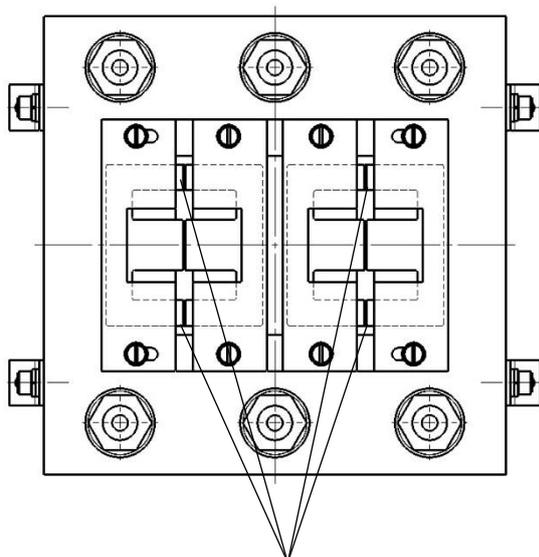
Draufsicht einer Drossel mit Luftspalteinlagen
